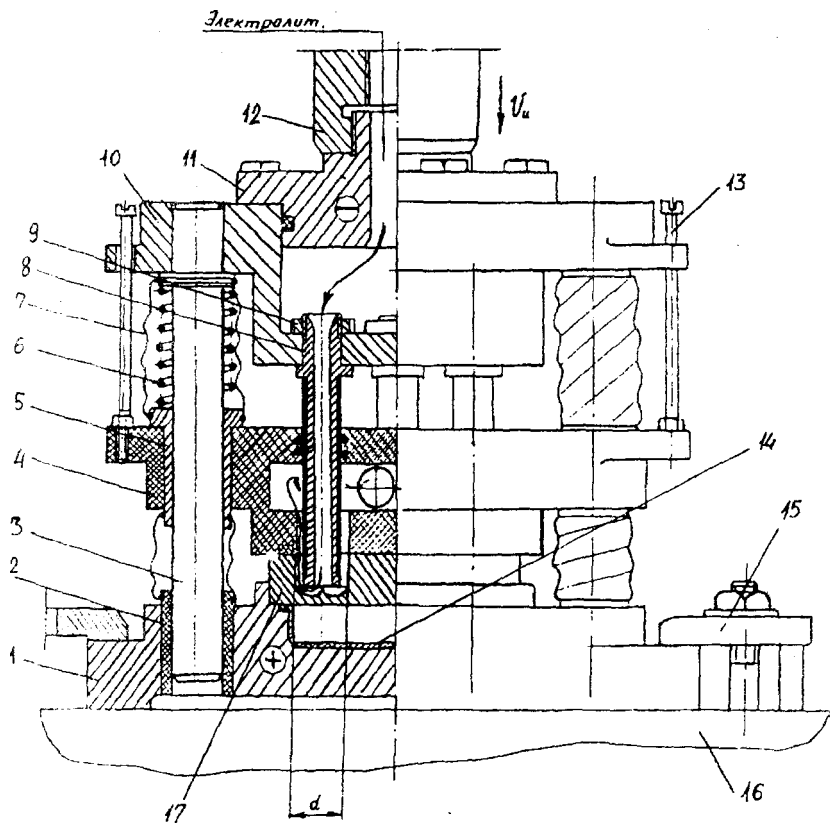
Приспособление для электрохимической прошивки отверстий
